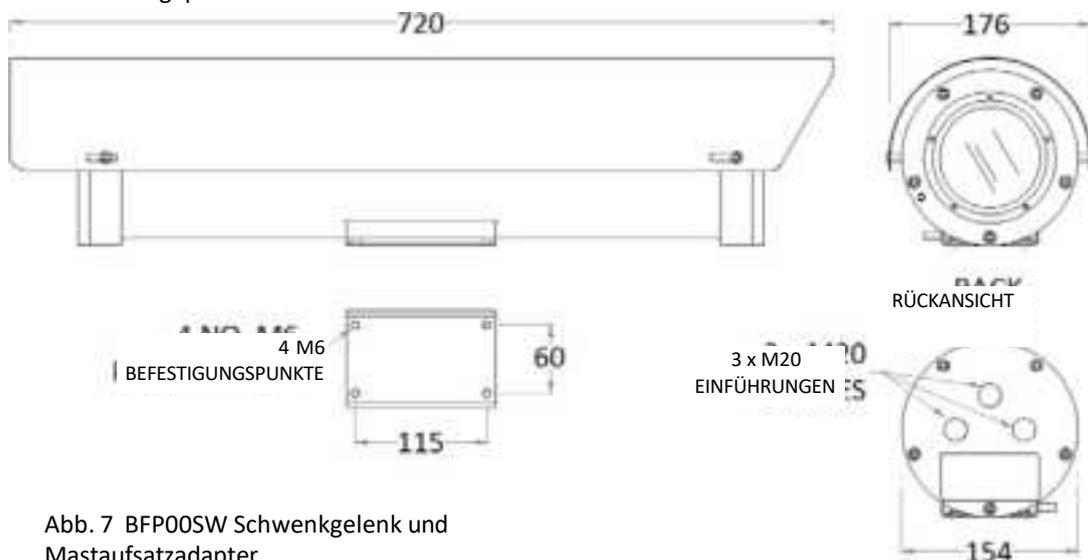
BFP00SW Schwenkgelenk und Mastaufsatzadapter
